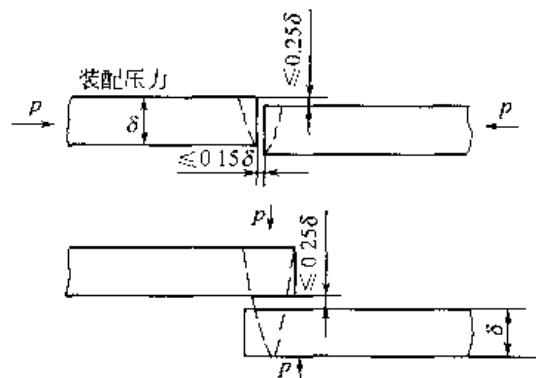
对接接头和搭接接头装配尺寸公差要求
